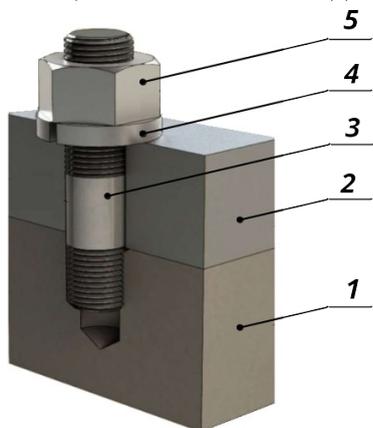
Соединение деталей шпилькой: 1 и 2 – соединяемые детали, 3 – шпилька, 4 – шайба, 5 – гайка
